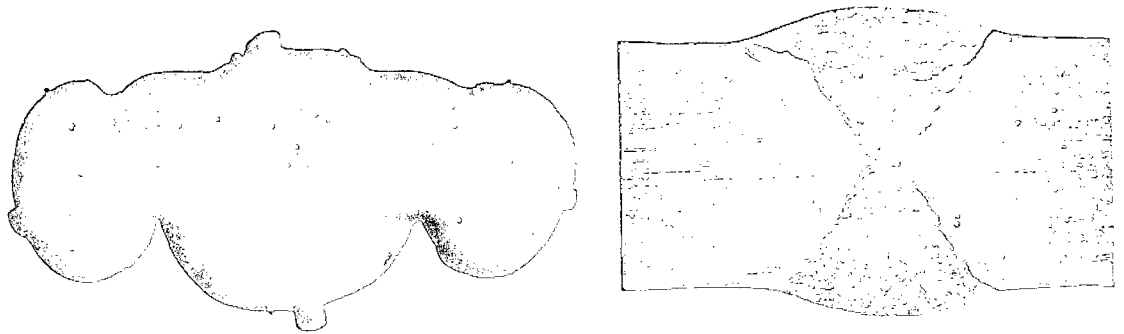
Macrografía de soldaduras sin defecto alguno. Estas soldaduras han sido realizadas siguiendo las recomendaciones generales descritas.
